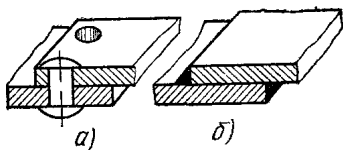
Сравнение клепаного и сварного соединения:
